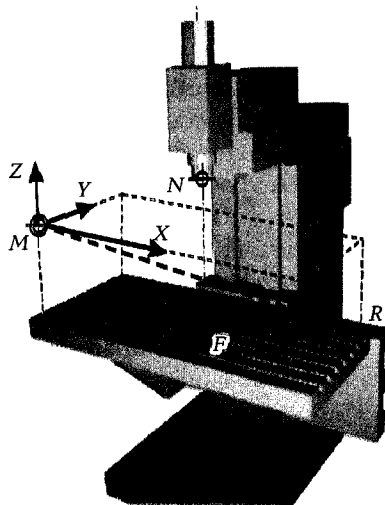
Позиция нулевой точки M на фрезерном станке:
